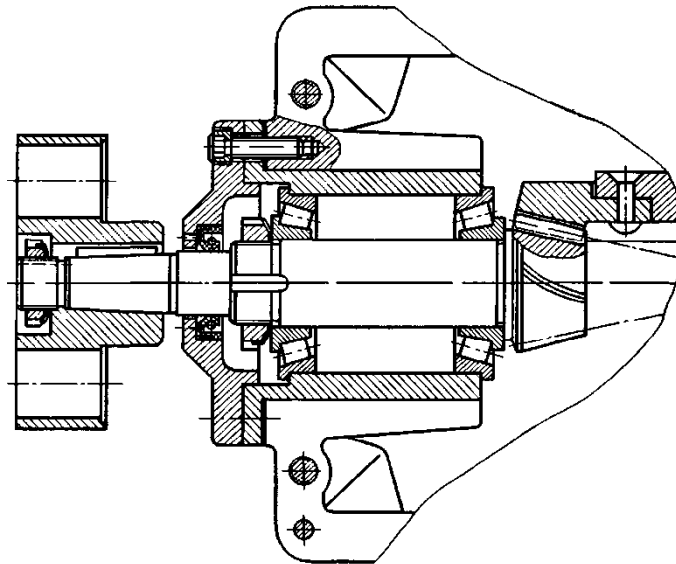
Установка конических роликоподшипников по схеме 4 – растяжку; обе опоры фиксирующие, крышка торцовая, регулирование подшипников – круглой илицевой гайкой.
